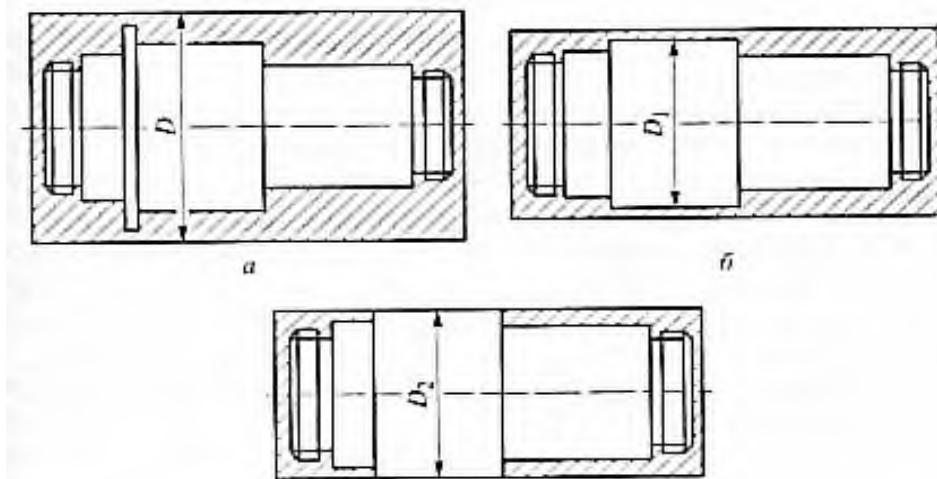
Деталь, изготавливаемая из сортового профиля [7]
